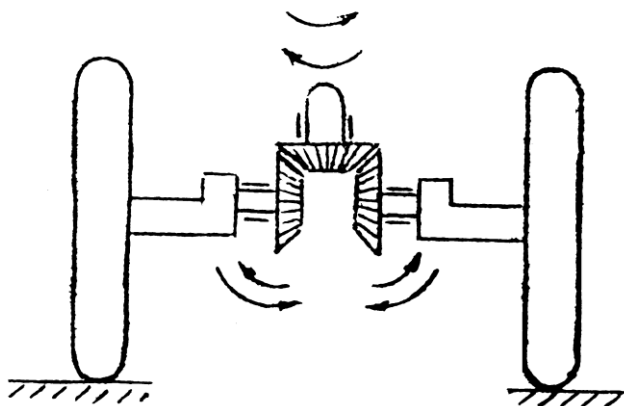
Схема зубчастого механізму самоустановлення нижнього станка
